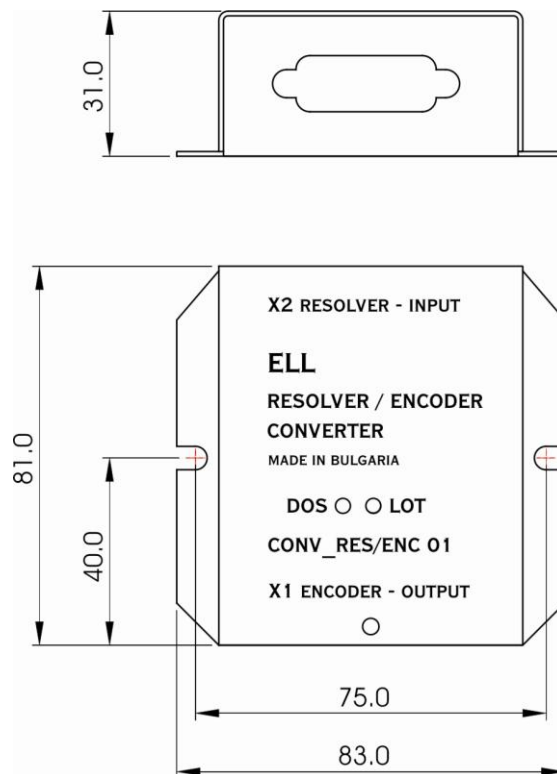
Присоединительные и габаритные размеры CONV_RES/ENC 01
